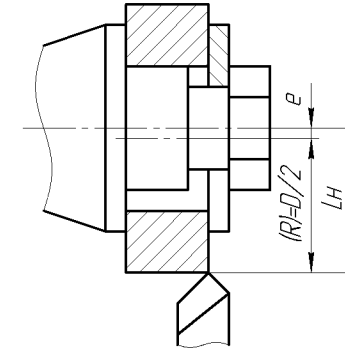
Визначення похибки базування при базуванні заготовки по циліндричному отвору
